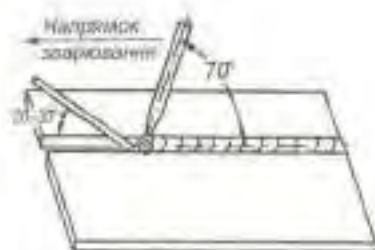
Зварювання тонких листів з подачею присаджувального металу в дугу
